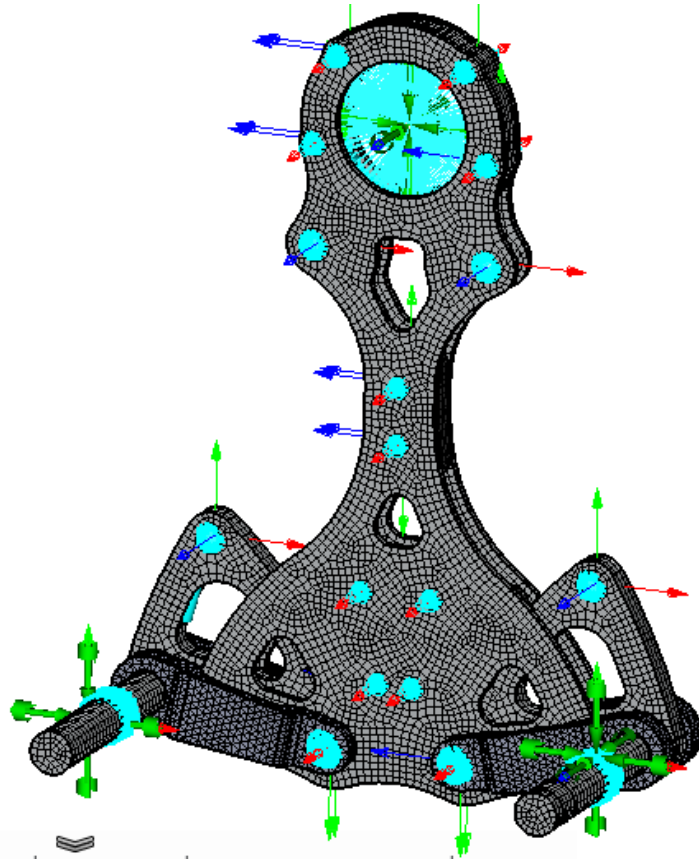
Conexiones y restricciones del conjunto con ejes. Restricción en los ejes
